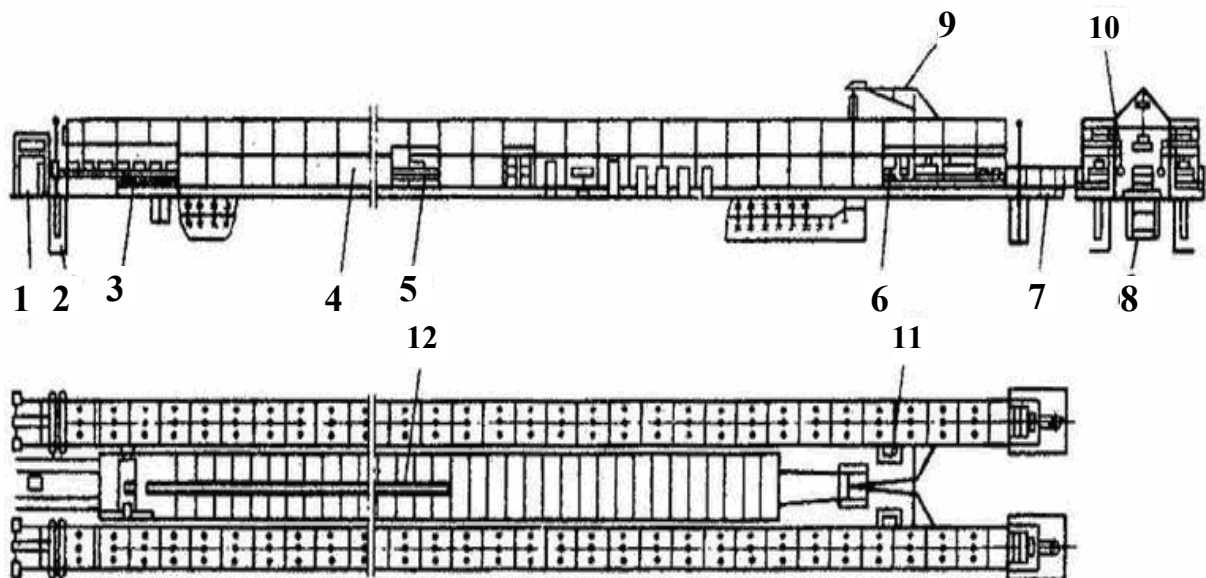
Схема ливарно-підв'ялювального конвеєра: 1 – гідроштовхач верхній; 2 – гідропідіймач; 3 – механізм зливу шлікера; 4 – камера; 5 – механізм заливання шлікера; 6 – візки; 7 – гідроштовхач нижній; 8 – підв'ялювальний конвеєр; 9 – пневмопідіймач; 10 – монорельс прибирання відходів; 11 – механізм знімання виробів; 12 – конвеєр повернення воронки і кілочків
